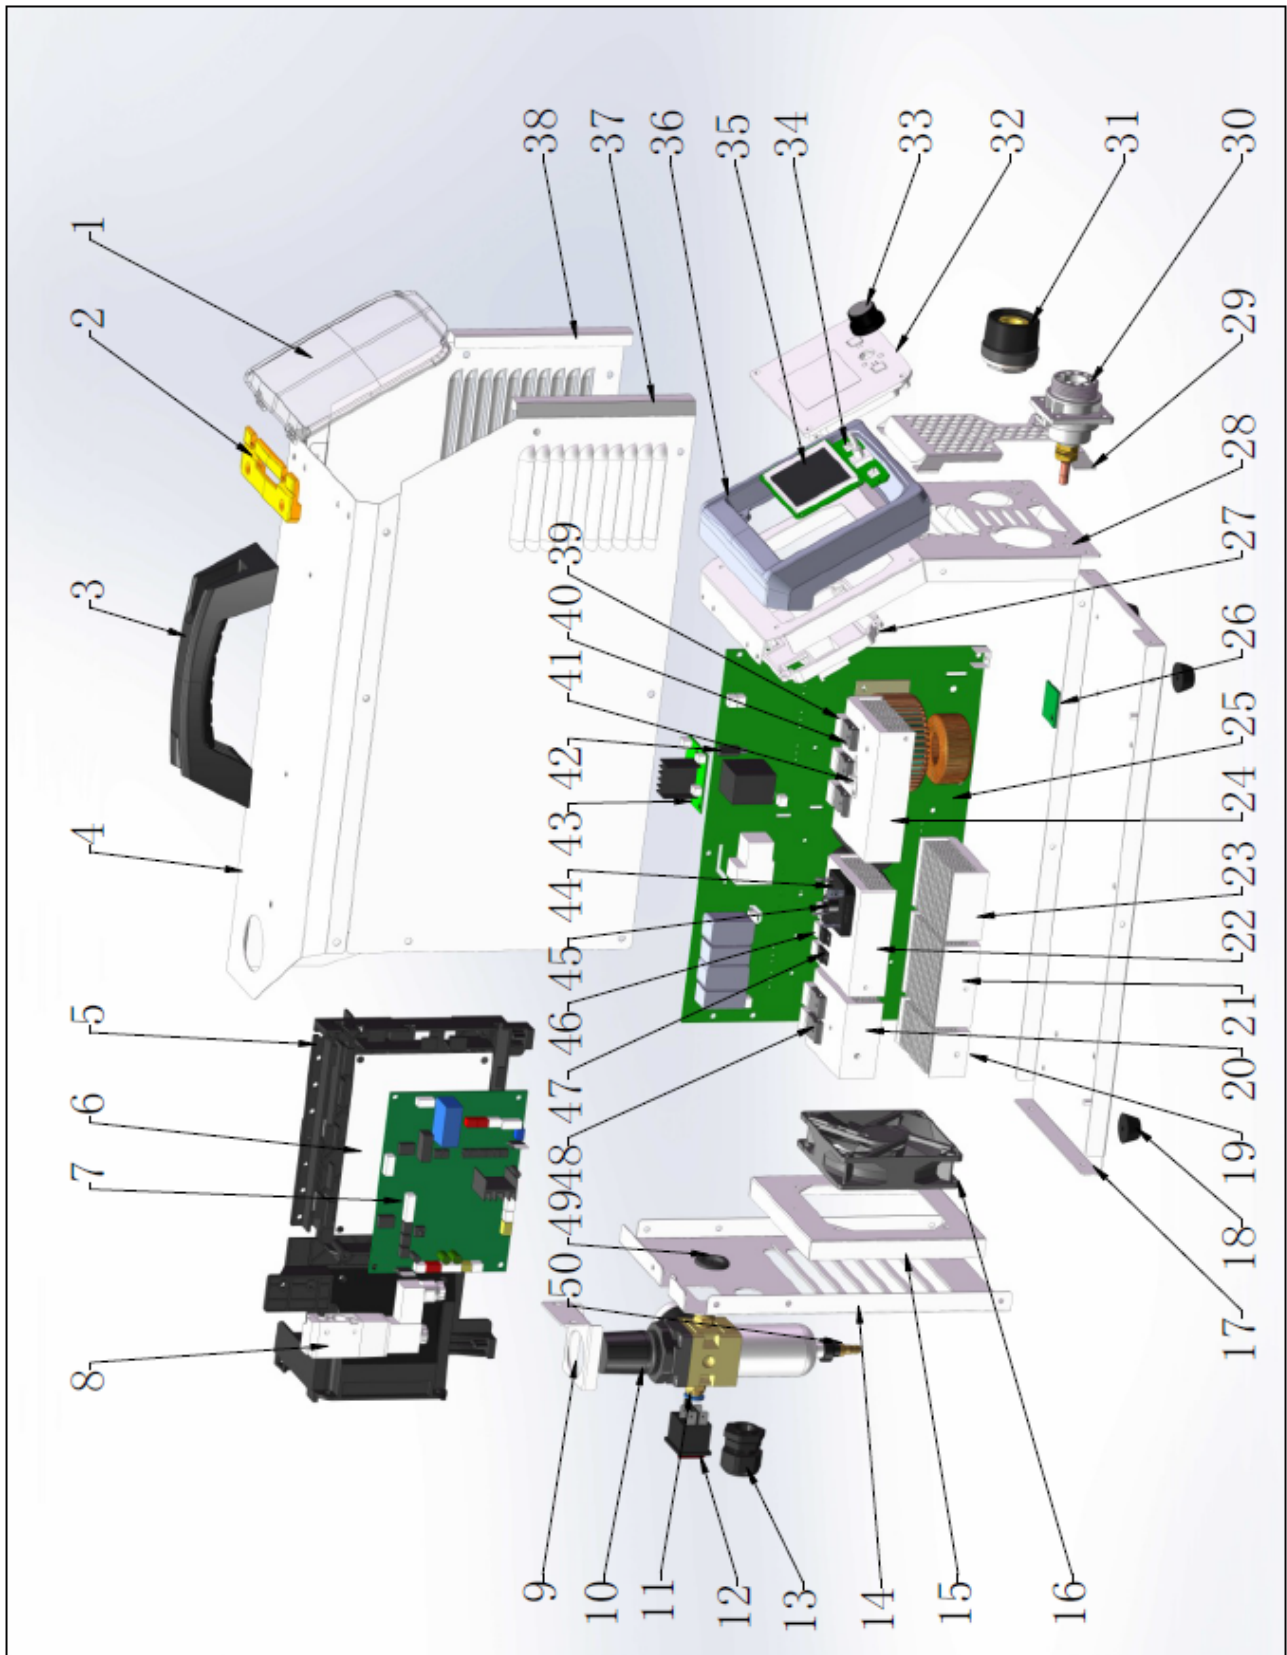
Ersatzteilzeichnung CRAFT-CUT 41P LCD
